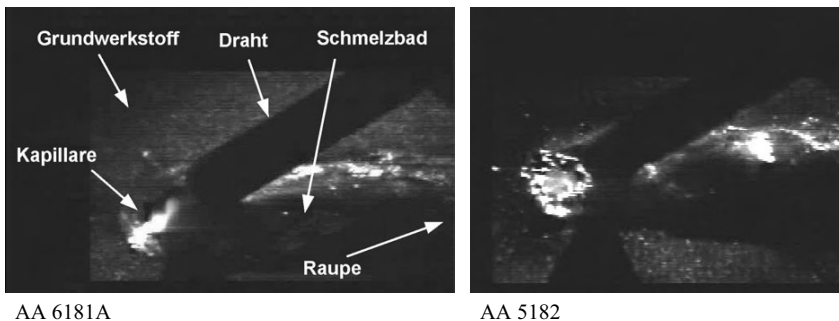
Standbild Referenz-Schweißprozess mit stechender Drahtzuführung
